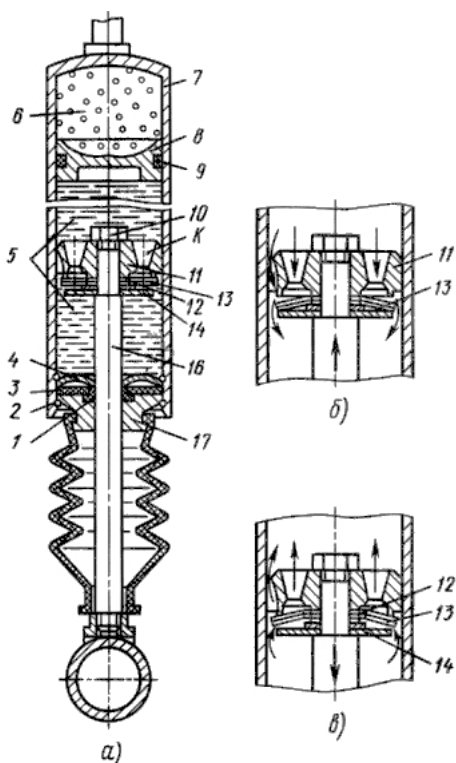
Однотрубный газонаполненный амортизатор и схема его работы: *а* — конструкция; *б* — схема работы при сжатии; *в* — схема работы при отдаче; 1 — сальник; 2 — запорное кольцо; 3 — резиновая шайба; 4 — фасонная шайба; 5 — жидкость; 6 — газ; 7 — корпус; 8 — плавающий поршень; 9 — сальник; 10 — гайка; 11 — поршень; 12 — звездочка; 13 — диск; 14 — шайба; 15 — шайба; 16 — шток; 17 — направляющая штока
